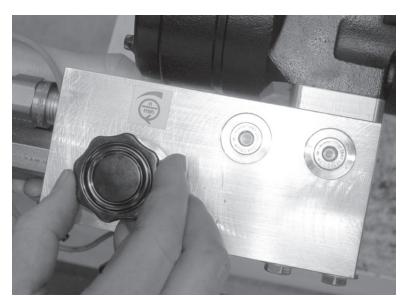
Поворачивайте шкалу на гидравлической клапанной коробке для регулирования частоты вращения станка.
